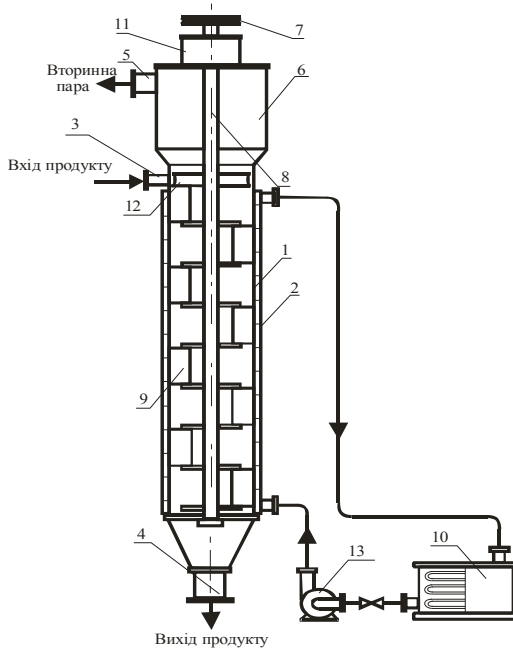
Установка роторного плівкового апарата: 1 – корпус апарата; 2 – теплова оболонка; 3 – патрубок входу продукту; 4 – патрубок виходу продукту; 5 – вихід вторинної пари; 6 – сепаратор; 7 – привідний шків; 8 – вал ротора; 9 – шарнірна лопать; 10 – місткість із тенами; 11 – підшипниковий вузол; 12 – розподільне кільце; 13 – циркуляційний насос
